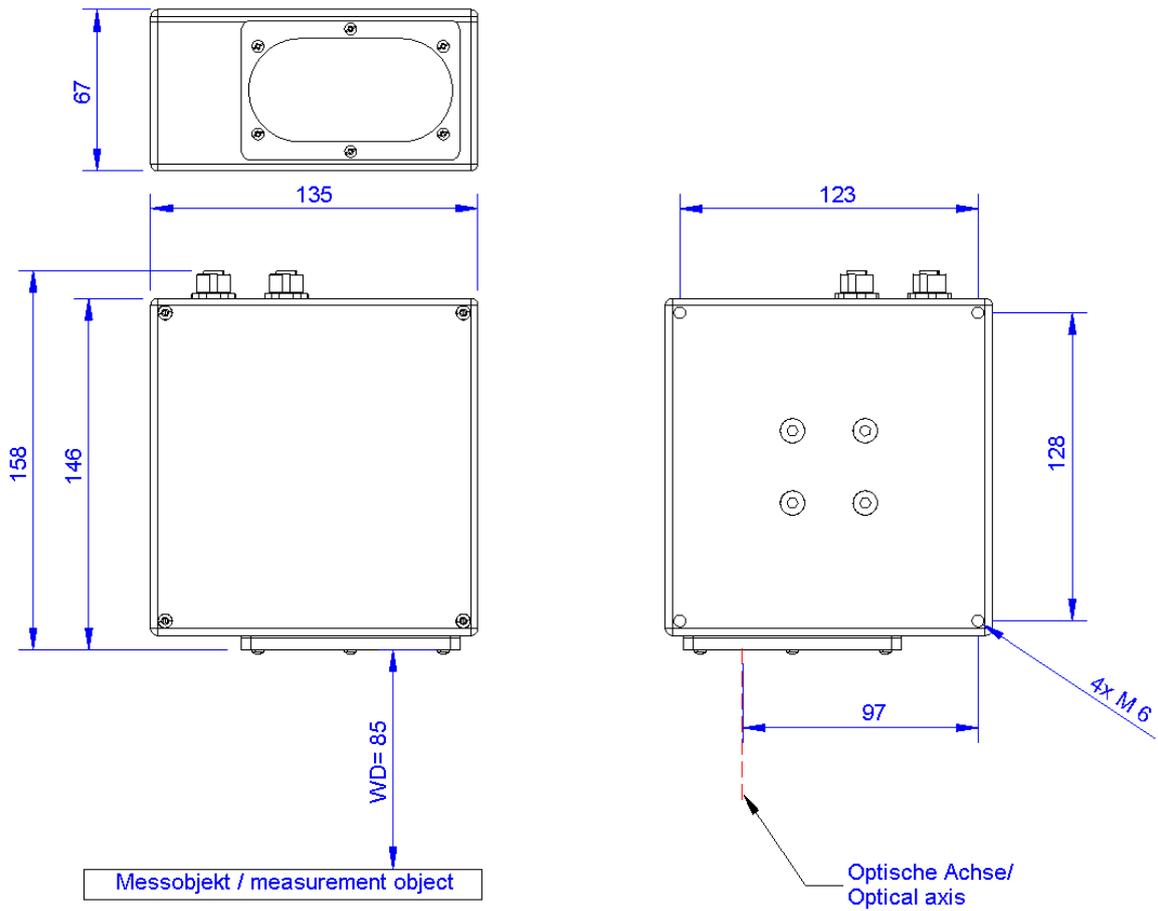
Maß- und Einbauzeichnung des VLM502 - O
